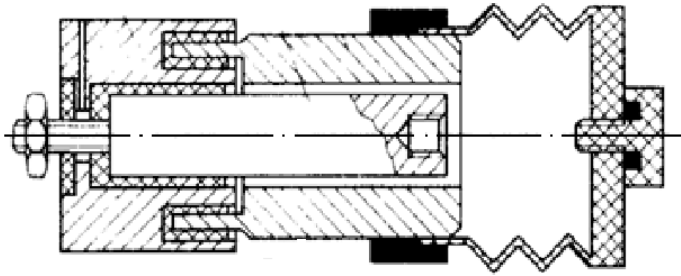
Измерительный конденсатор с цилиндрическим зазором [243]
